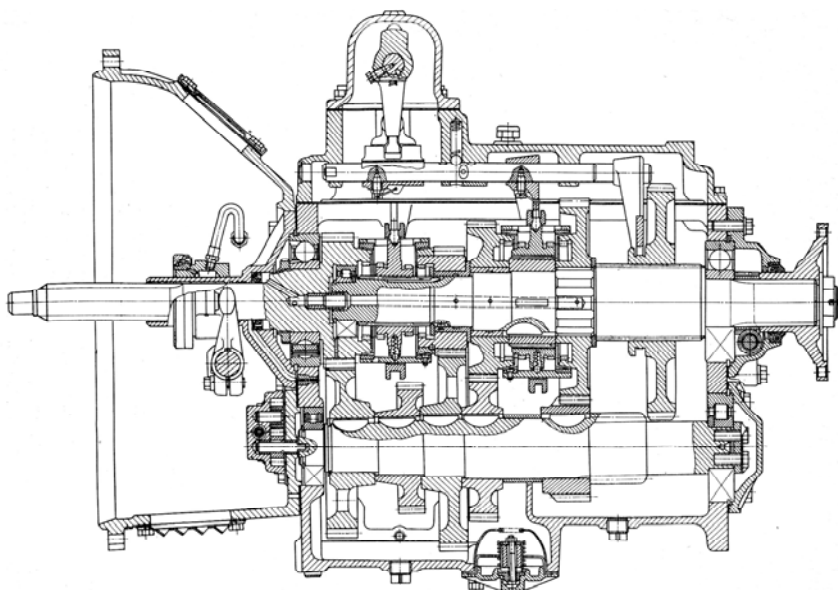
Коробка передач автомобиля МАЗ-500А
